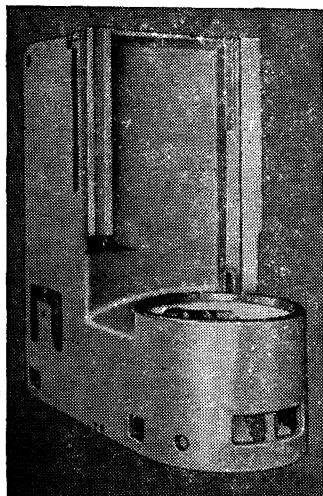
Монолитная конструкция станины со столом одностоечного станка фирмы Bullard
